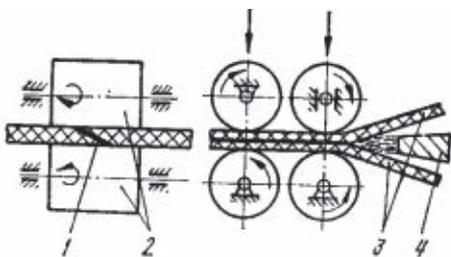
Схема сварки нагретым газом листов термопласта без присадочного материала: 1 – сварной шов, 2 – прижимные ролики, 3 – свариваемые листы, 4 – наконечник нагревателя
